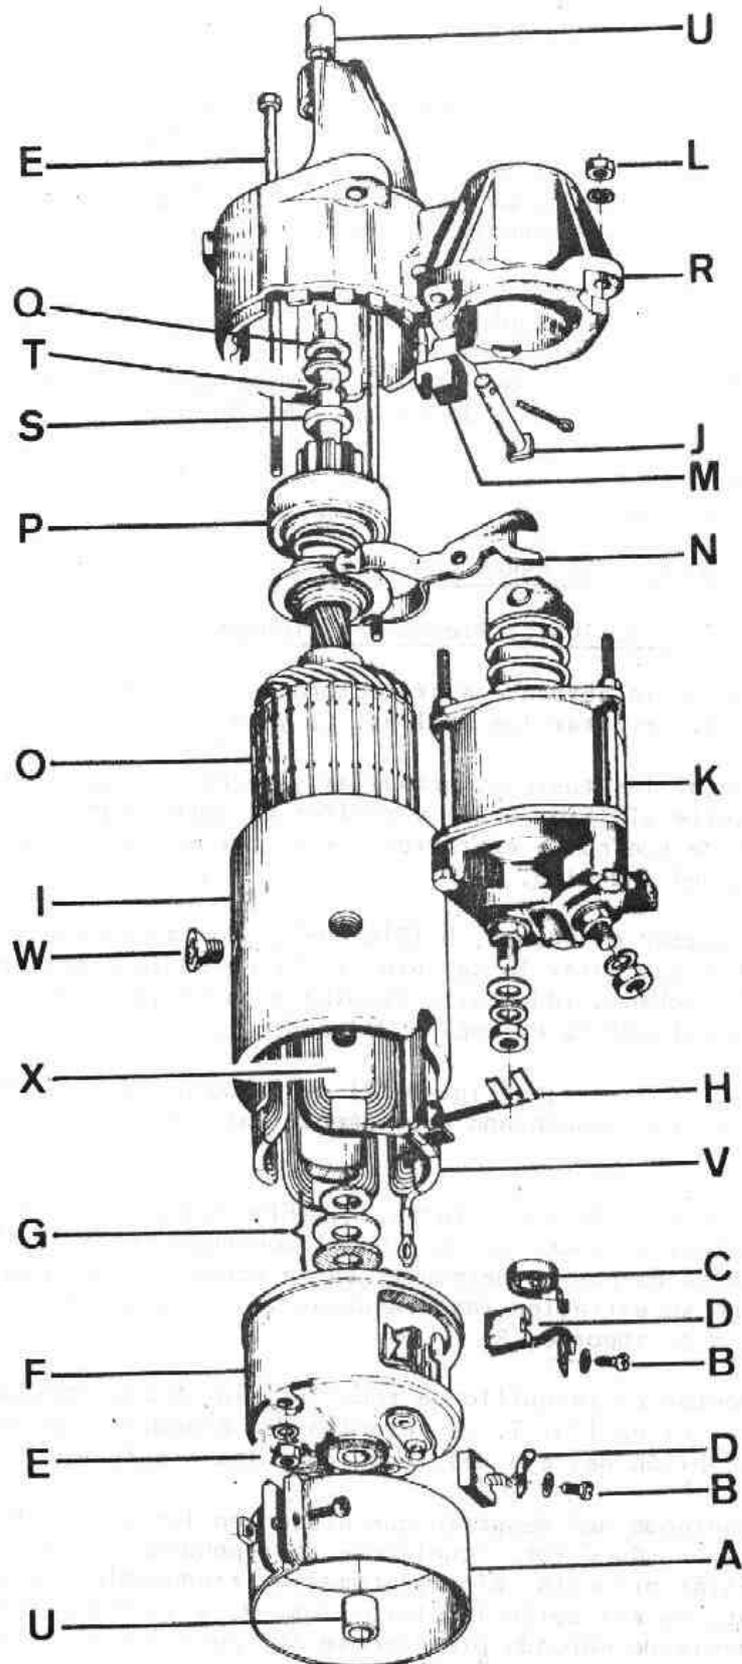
Despiece del motor de arranque MOE-12.9 para motores Diesel 2 1/4 L.
